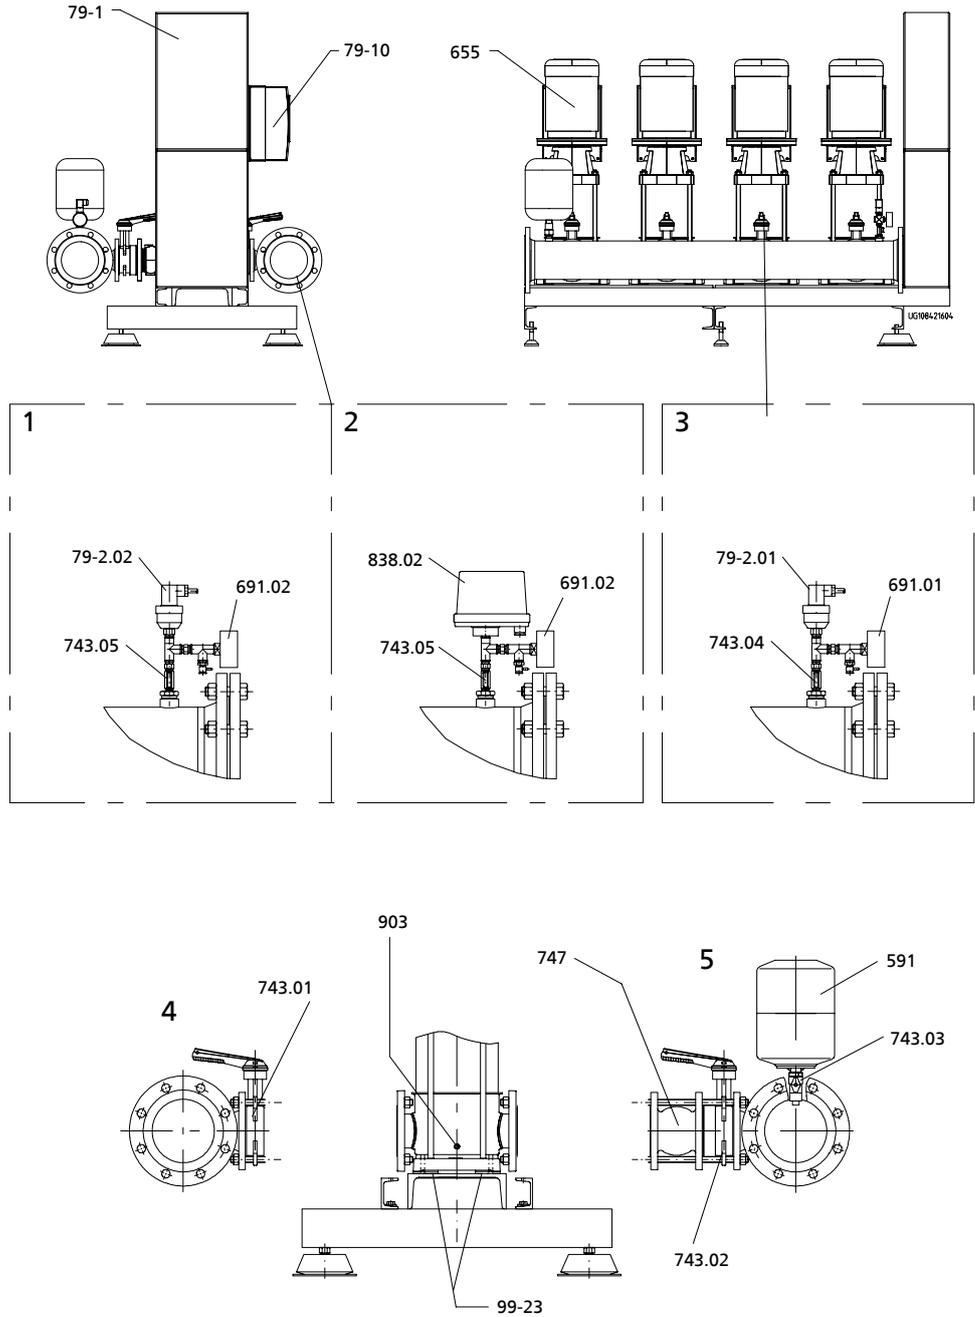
Gesamtzeichnung Hyamat SVP mit Movitec 25, 40, 60, 90
